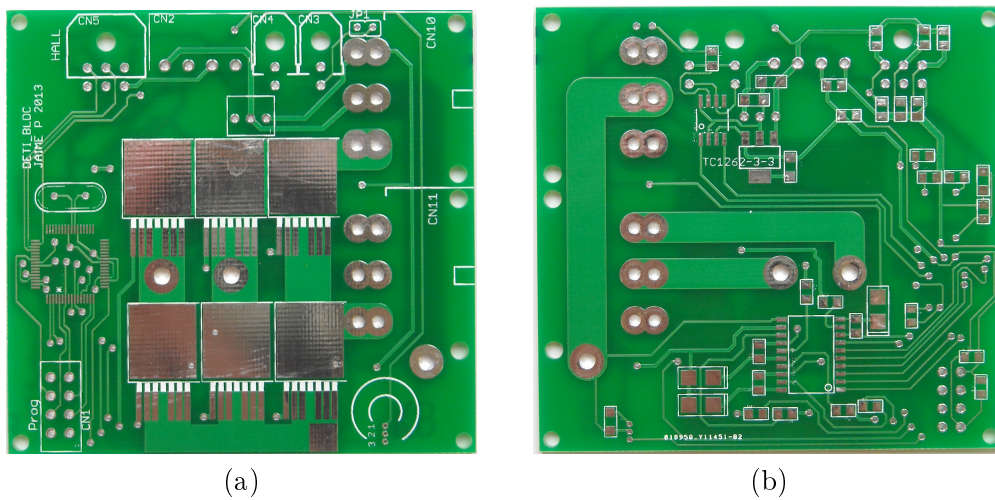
(a) PCB - Top (b) PCB - Bottom
